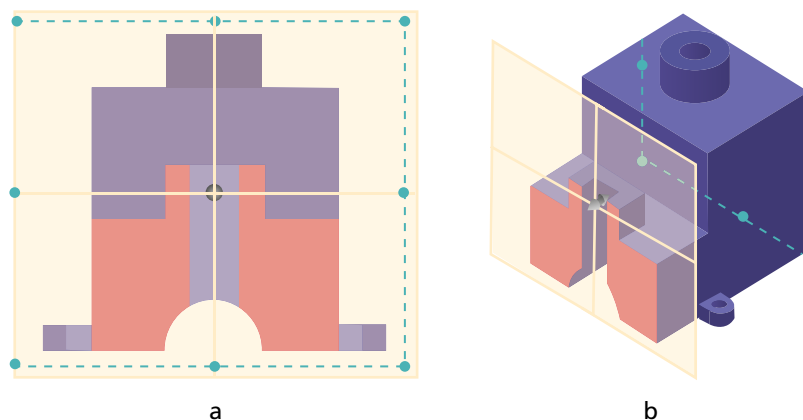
Corte total: a) proyección ortogonal de la vista lateral del corte total; b) plano de corte total paralelo al plano lateral
